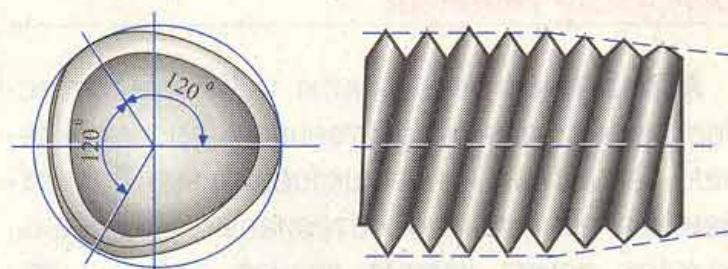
Трехгранное сечение стержня и вид заходной части резьбовыдавливающего болта.
